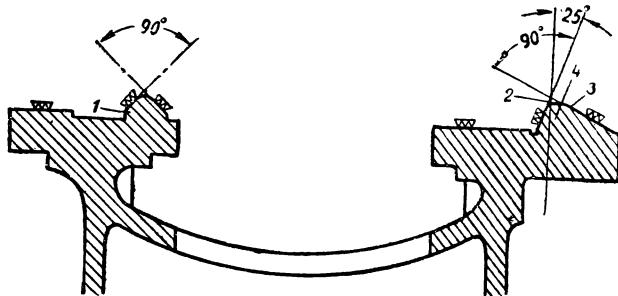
Плоские направляющие винторезно-токарного станка.
